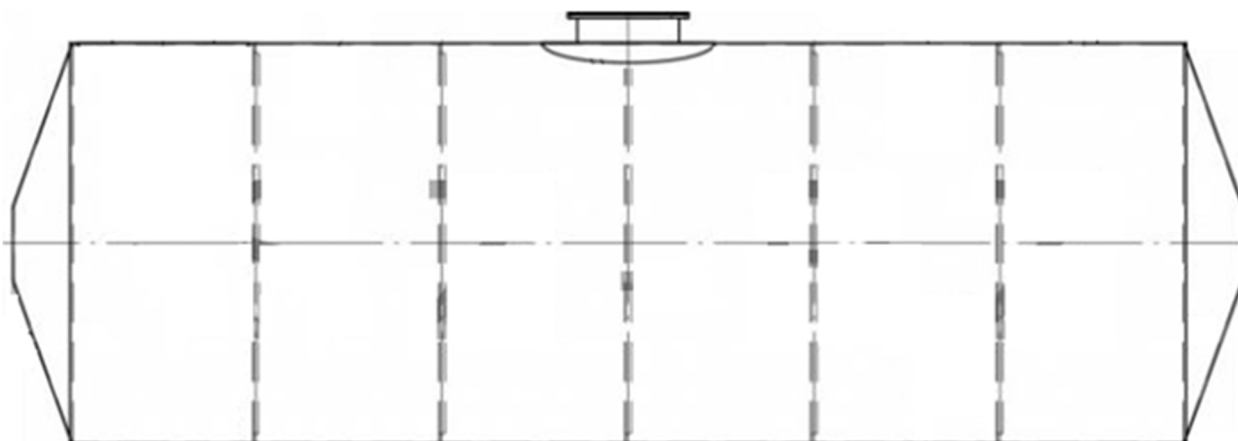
Эскиз общего вида резервуара РГС-70 заводской номер 58
